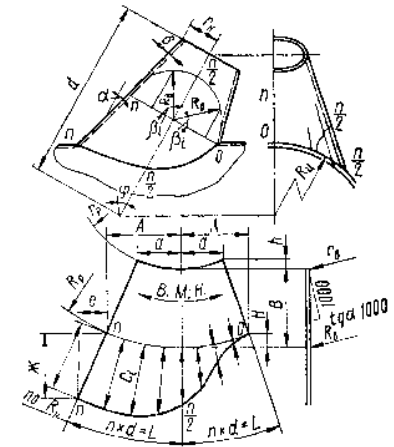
Наклонный конический штуцер на цилиндрической поверхности.
